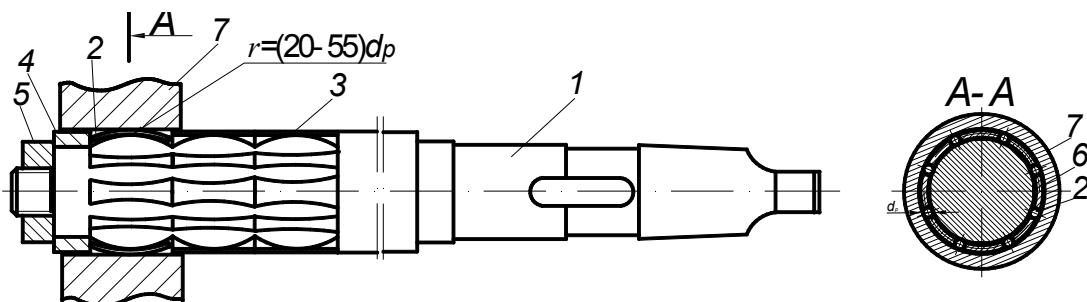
Пристрій для розкатування нежорстких втулок гнучкими роликами
